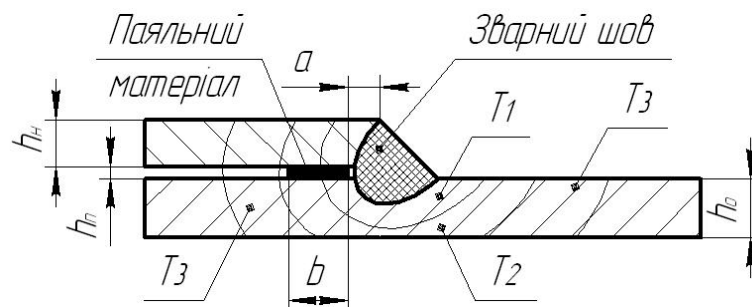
Варіант зварювання внапуск [авторська розробка]
